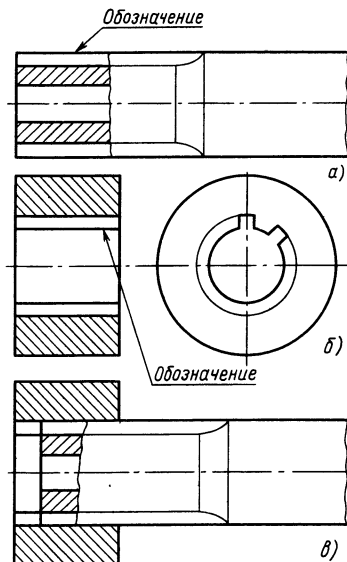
Шлицевое соединение: а — шлицевой вал; б — шлицевая втулка; в — соединение шлицевых деталей
